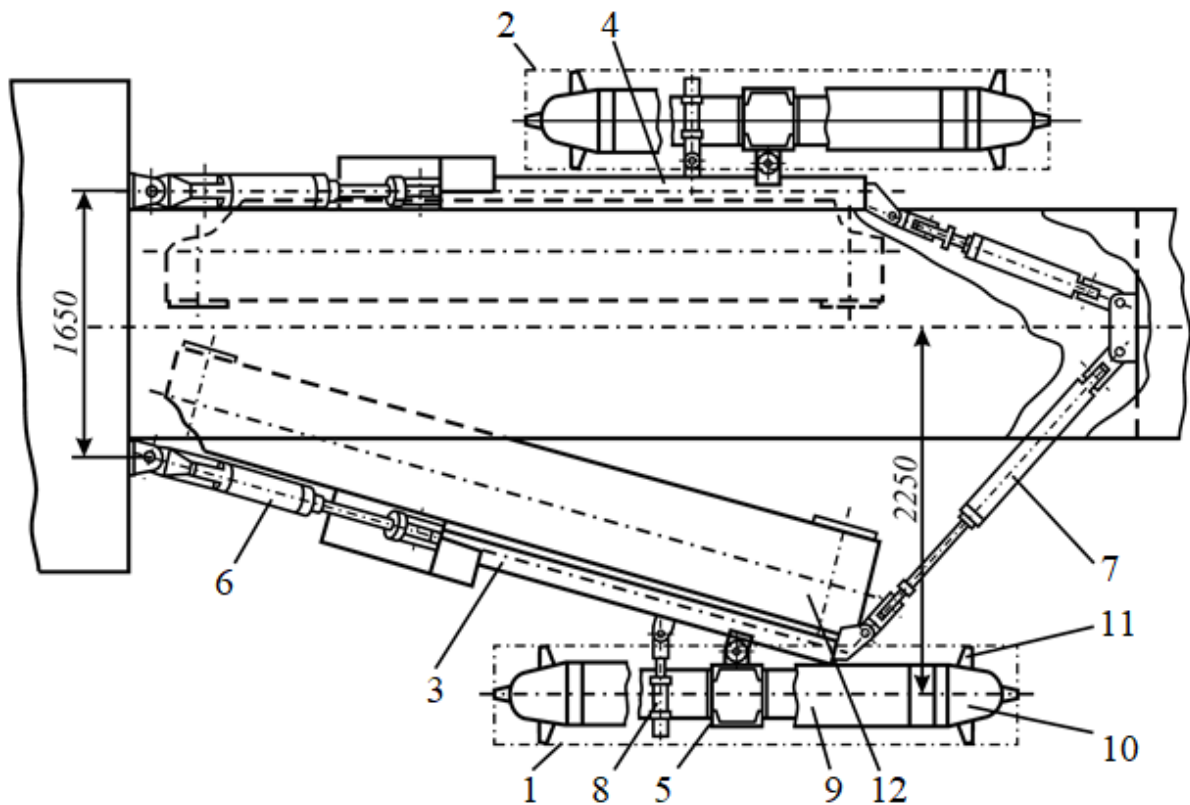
Роторний робочий орган машини ЩОМ-6Р:
